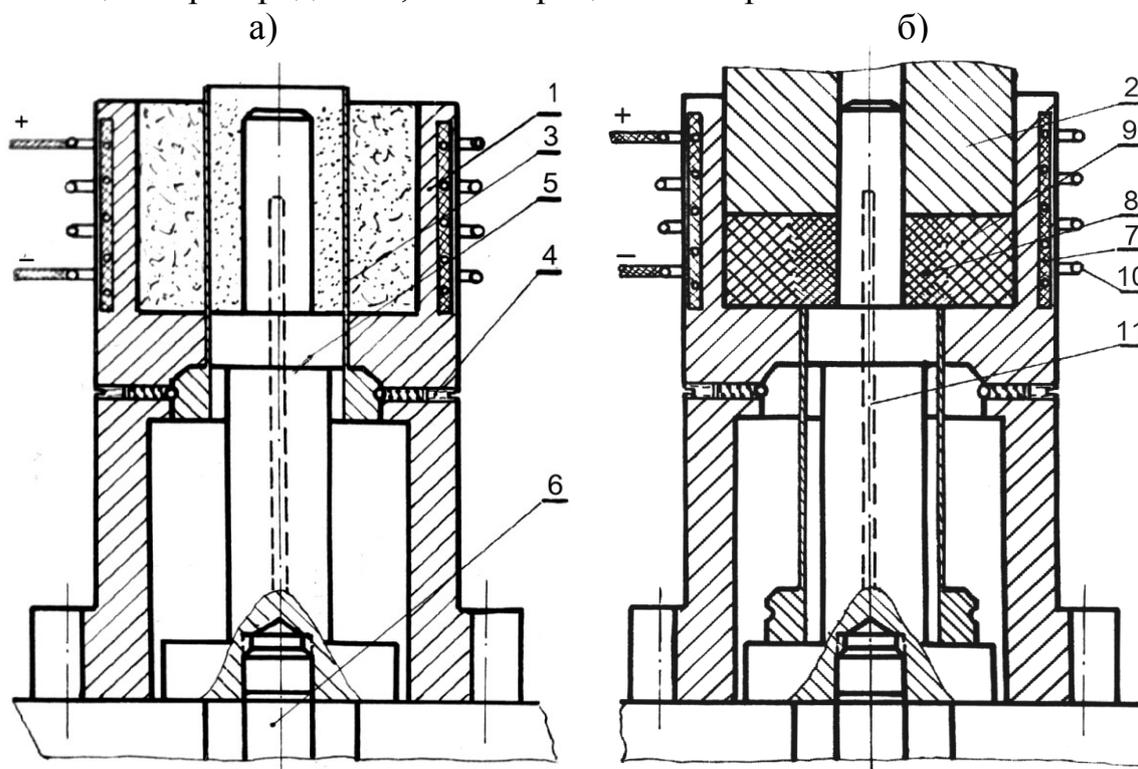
Схема устройства в начале (а) и конце (б) хода для прессования опор скольжения из нескольких пресс-композиций: 1 – матрица; 2 – пуансон; 3 – разделяющая перегородка; 4 – фиксаторы; 5 – опорная втулка; 6 – выталкиватель; 7 – термоизоляция; 8 – антифрикционная пресс-композиция; 9 – конструкционная пресс-композиция; 10 – омические нагреватели; 11 – термопара
